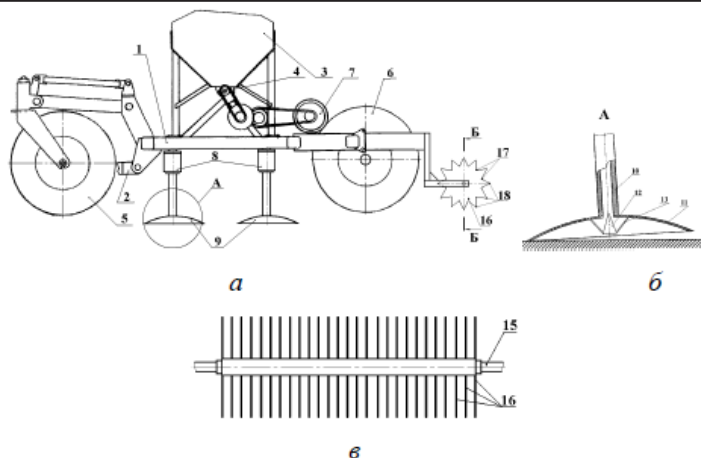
Комбинированный посевной агрегат (обозначения в тексте): а - вид сбоку; б – сошник; в – продольный разрез прикатывающего катка по линии Б-Б
